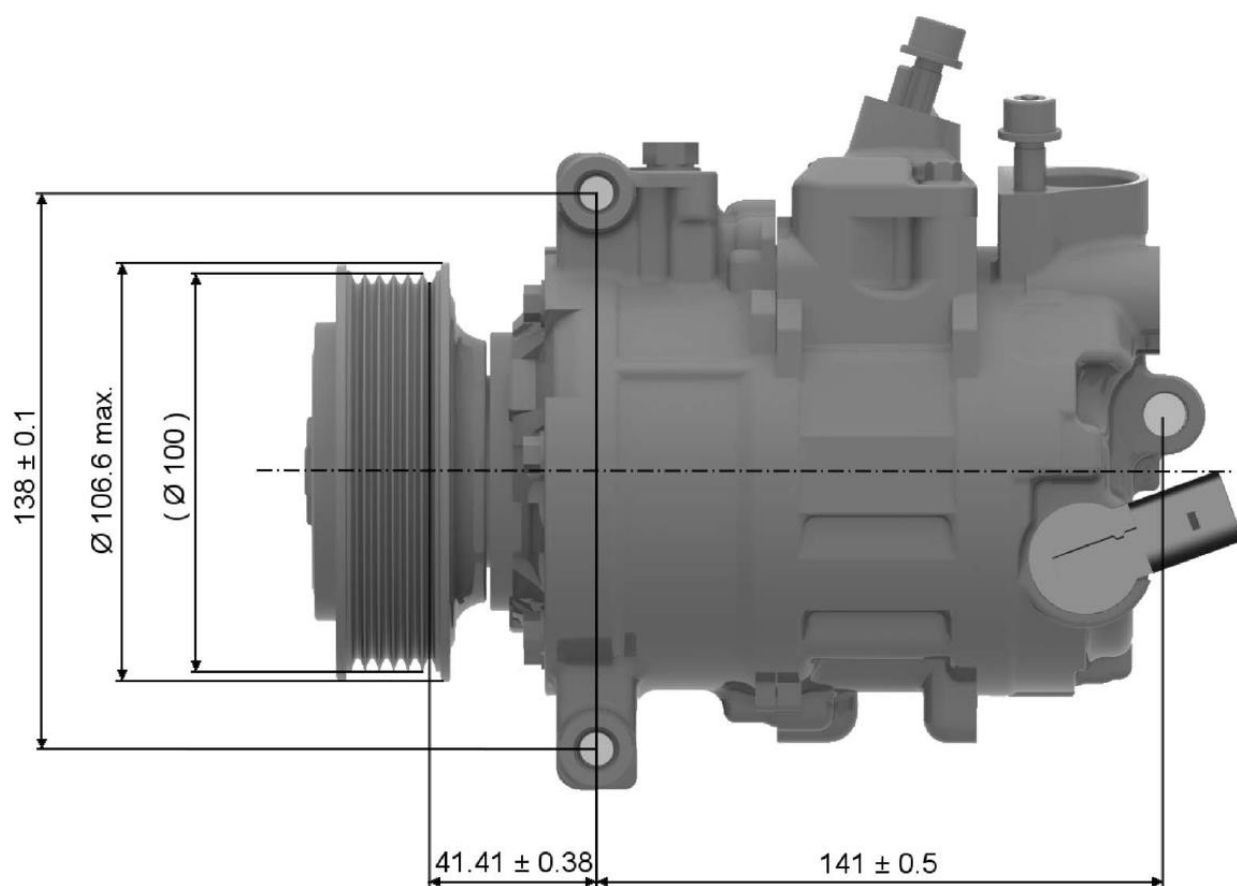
Размеры компрессора климатической установки DENSO-7SEU17, диаметр шкива 100 мм (вид сбоку)
